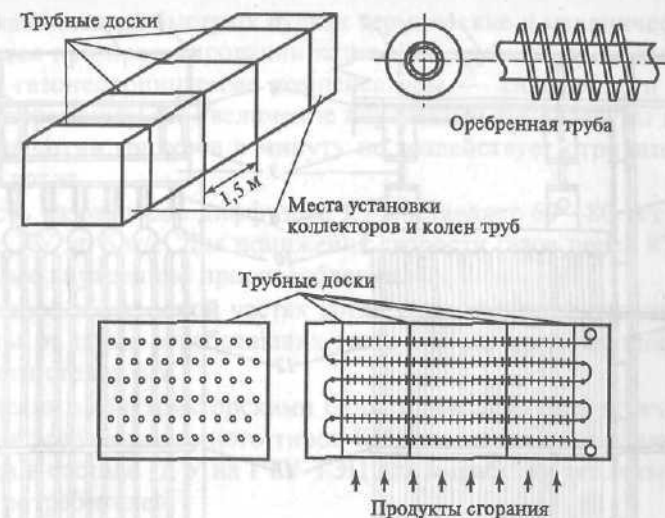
Компонка блока оребренных поверхностей нагрева вертикального КУ
